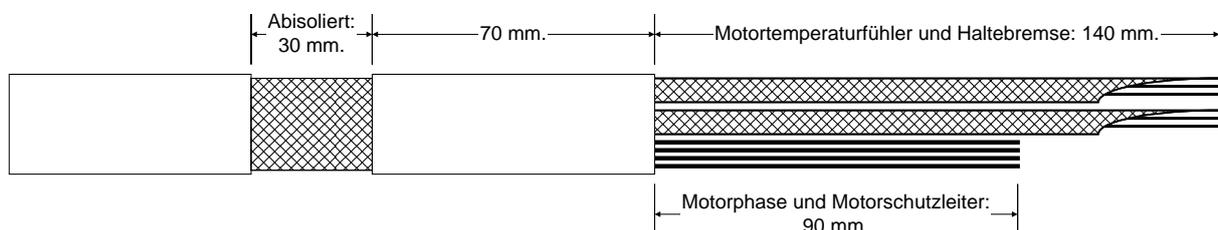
Motorkabel: Längen der Schirme und Leitungen
